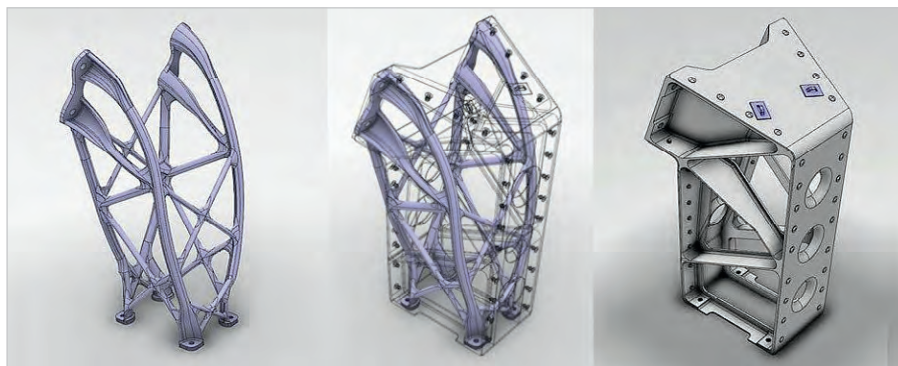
Стадии конструирования инновационного корпуса для крепления плат и моделей РЭА
